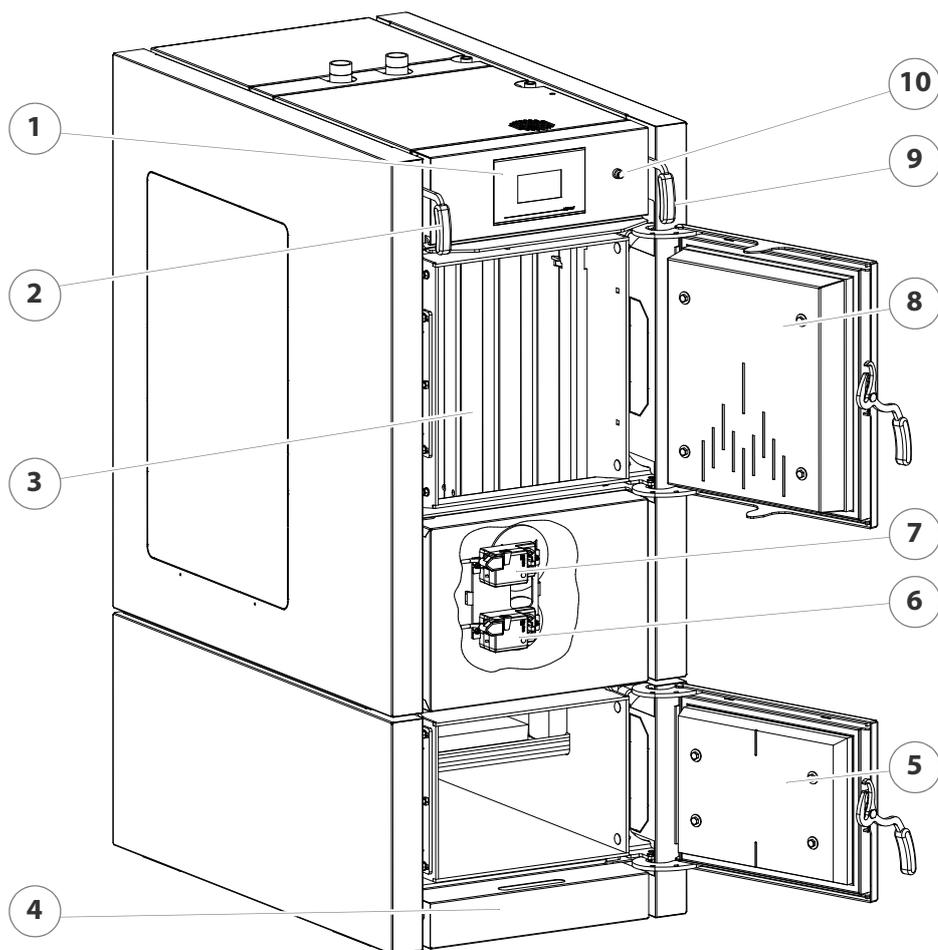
/1 - Frontansicht HDG F20-50 (E)
